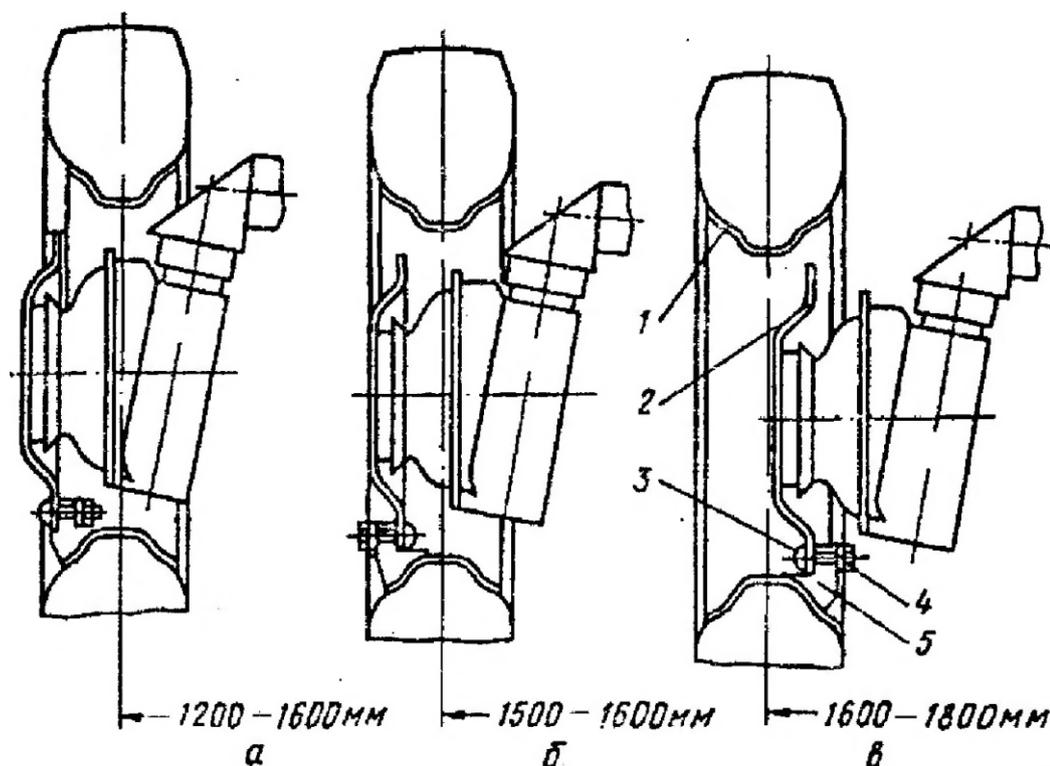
Схема установки передних колес тракторов МТЗ-82 и МТЗ-82Л на различную колею:
